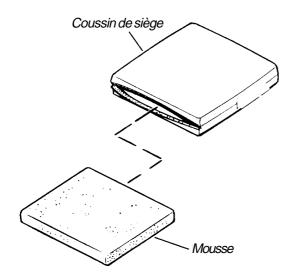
REMPLACEMENT DU COUSSIN DE SIEGE (INSERT EN MOUSSE)
